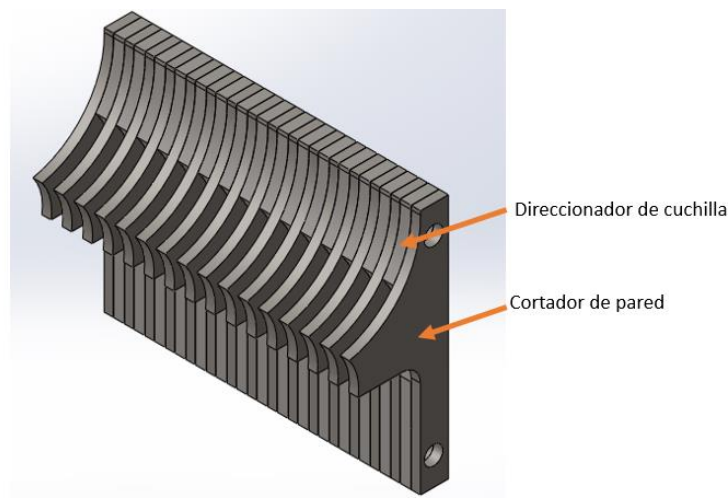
Ensamblaje del cortador de pared y direccionador de cuchilla
